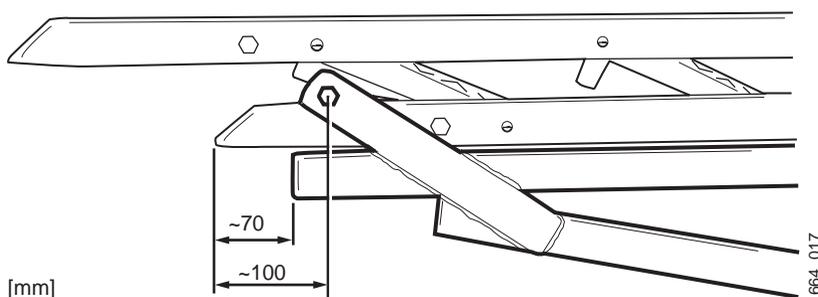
Vue détaillée de l'extrémité inférieure de la poutre, avec l'escalier en place
